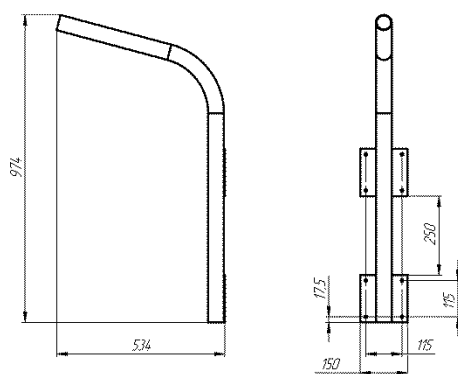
Кронштейн для крепления светильника на бетонное ограждение "Контур-К-10".
